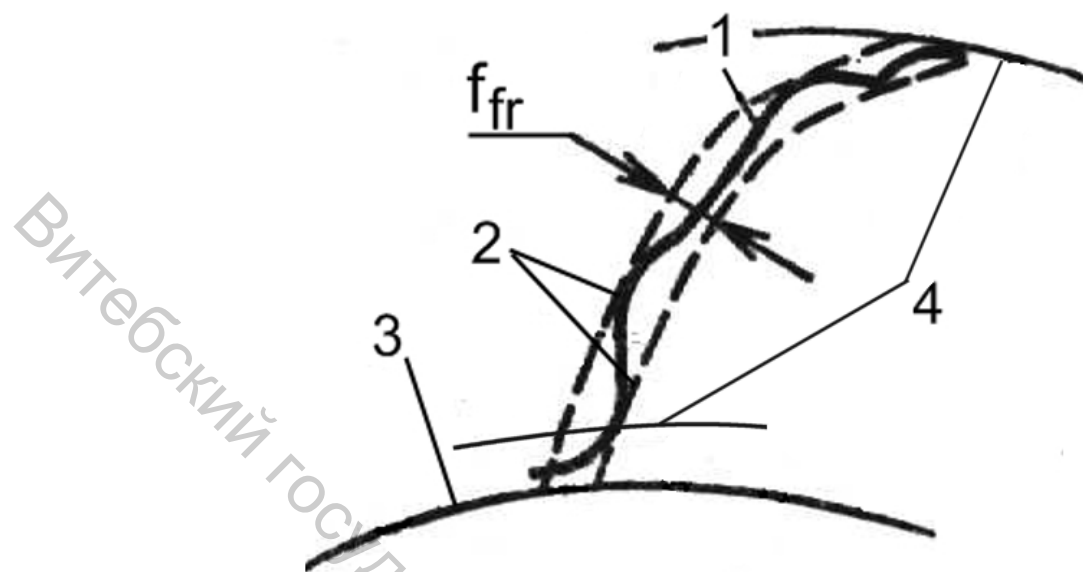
Схема для определения погрешности профиля зуба
